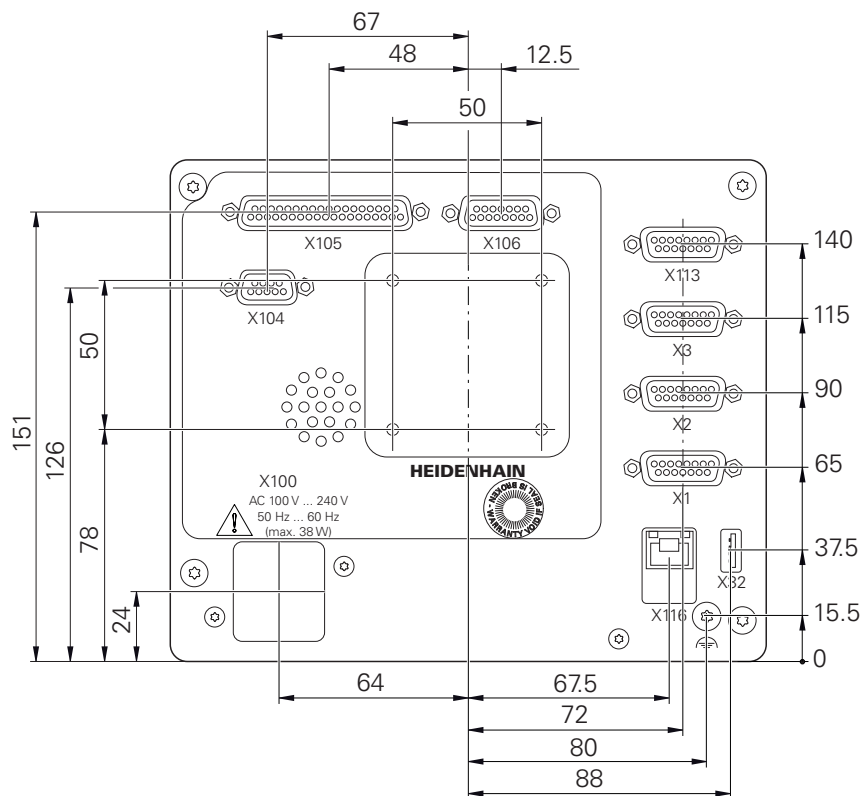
Dimensionering av enhetens baksida för enheterna med ID 1089179-xx
